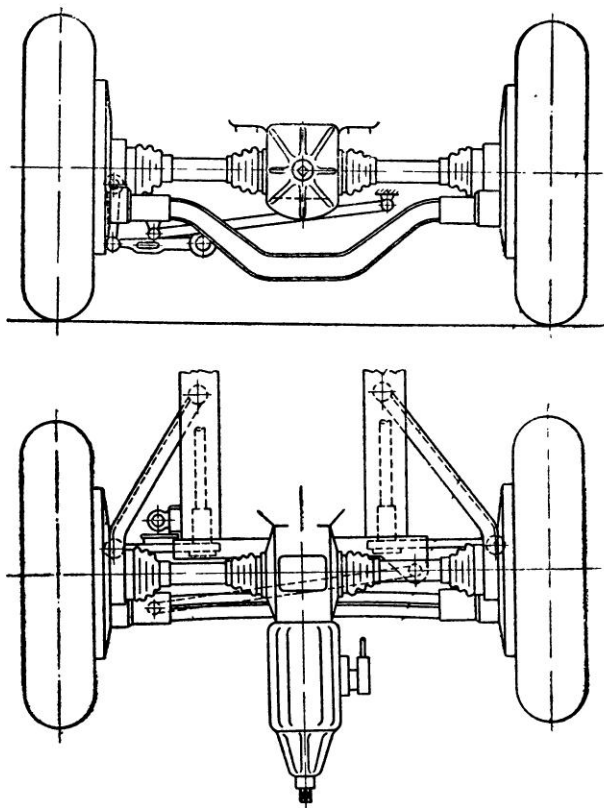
Схема подвески с неизменной шириной колеи задних колес и с реактивной штангой
